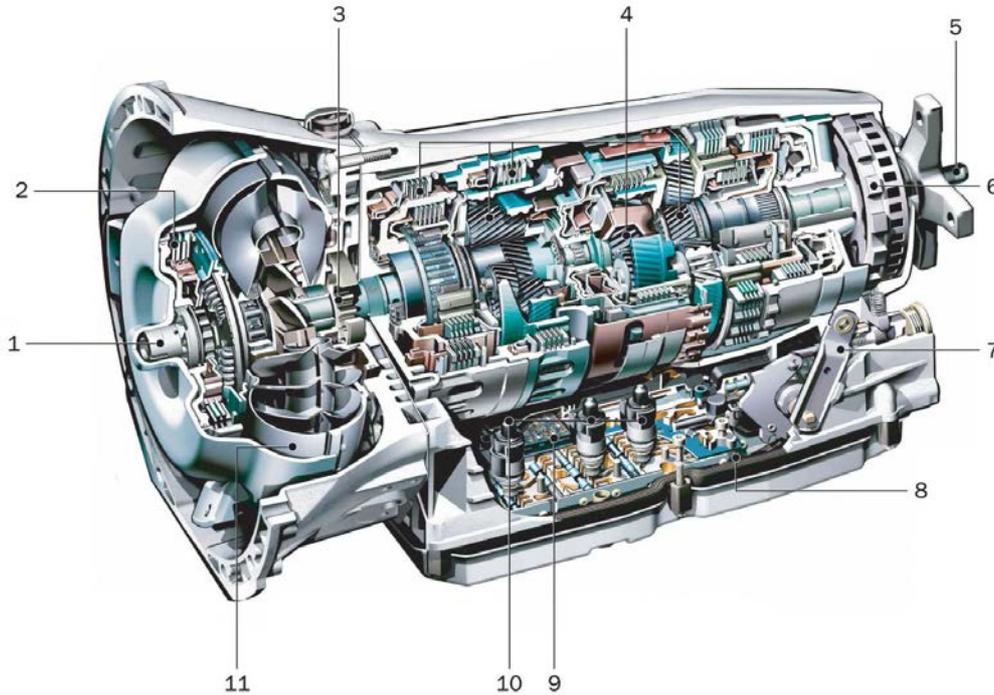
Устройство автоматической коробки передач «7G-Tronic» [3; 4]:
